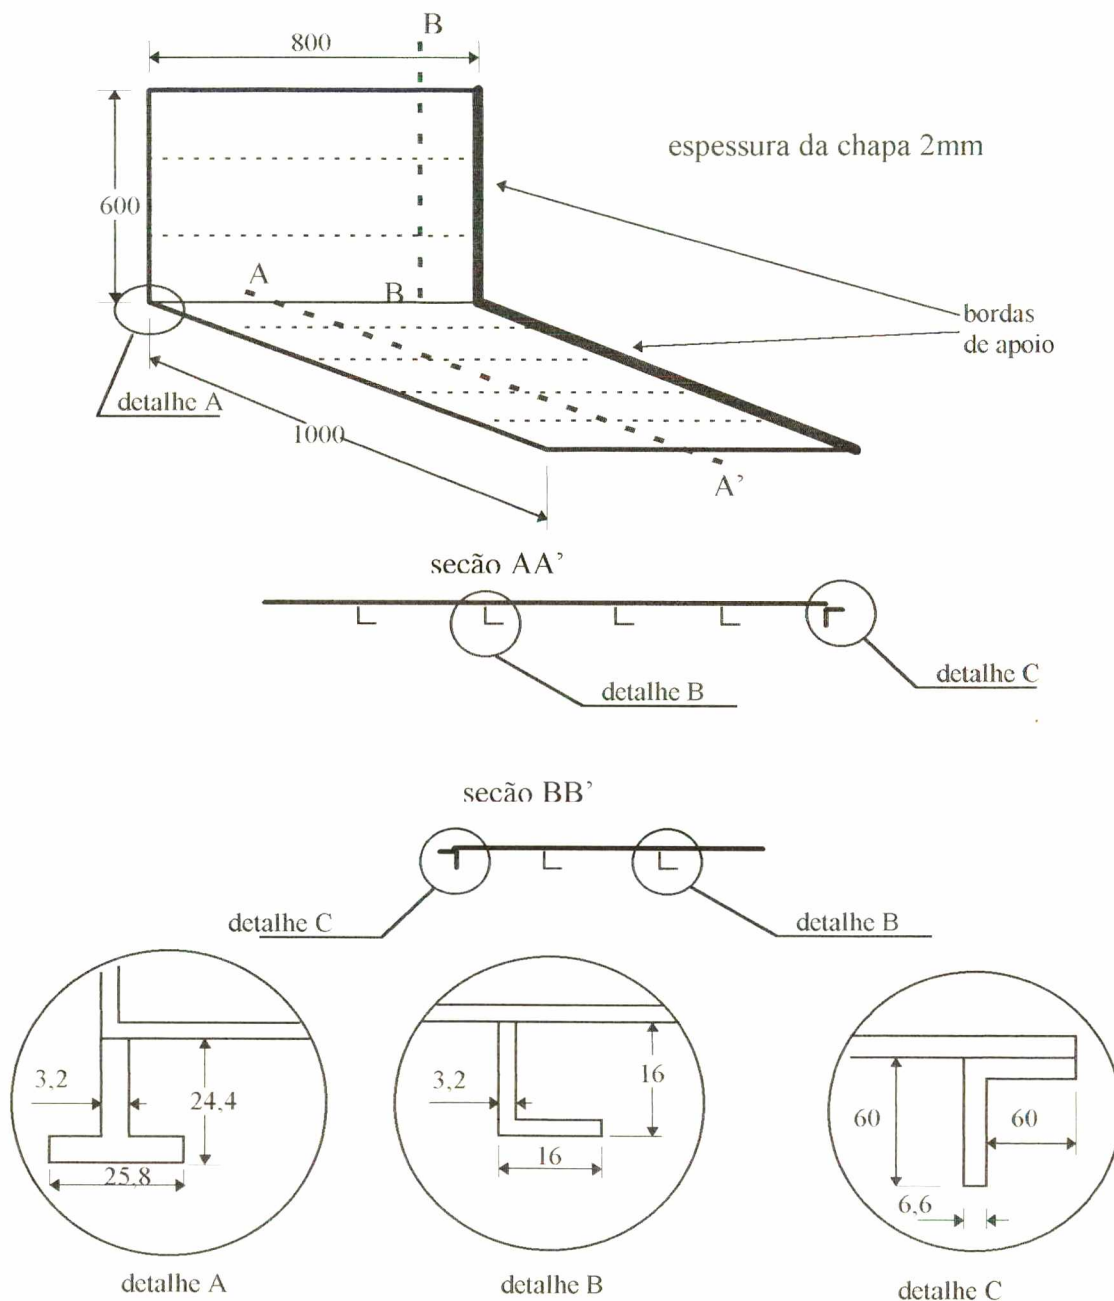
Desenho esquemático das placas com vigas paralelas(dimensões em mm).
